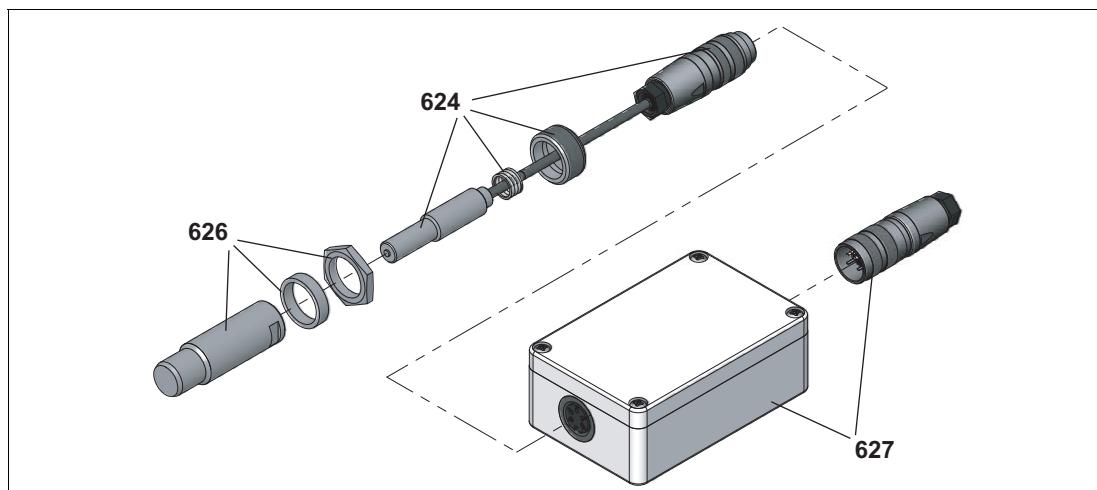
Explosionszeichnung BEG 45 + BEV 13
